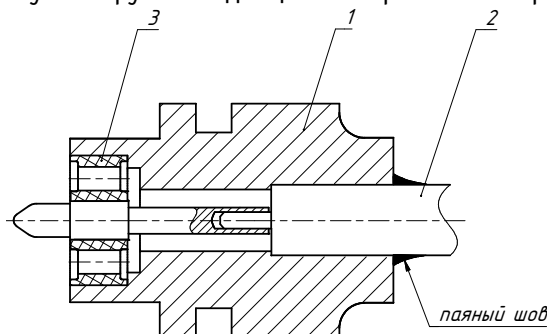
Запрессовка диэлектрической опоры в кабельный соединитель
